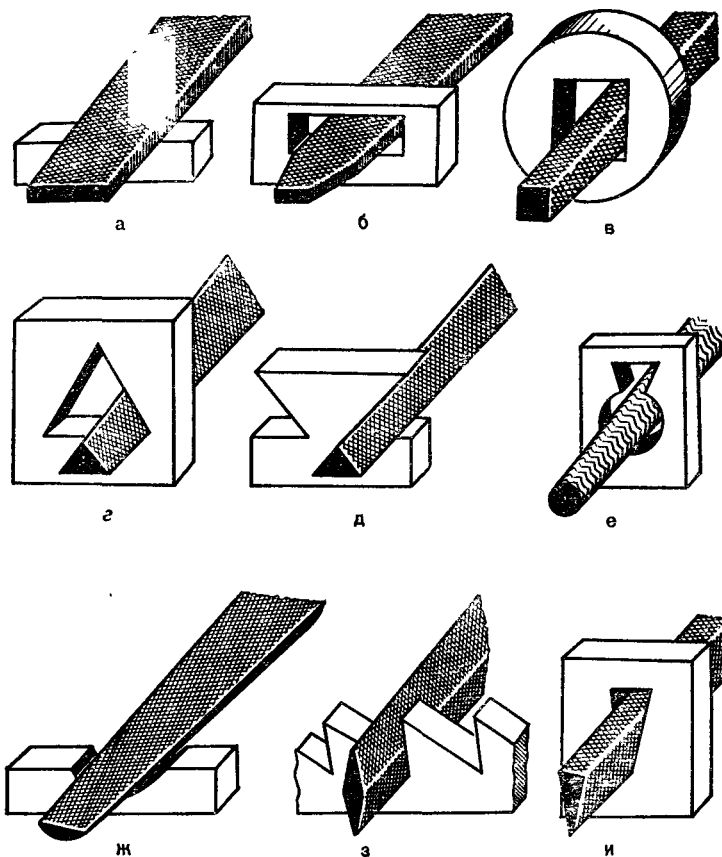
Виды напильников по форме поперечного сечения: а, б — плоские; в — квадратный; г, д — трехгранный; е — круглый; ж — полукруглый; з — ромбический; и — ножовочный.
